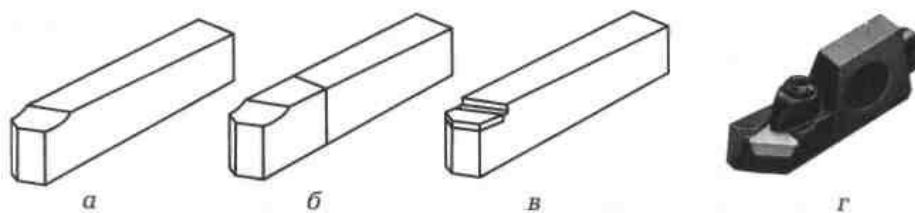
Типы резцов, определяемые по способу крепления их режущей части:
